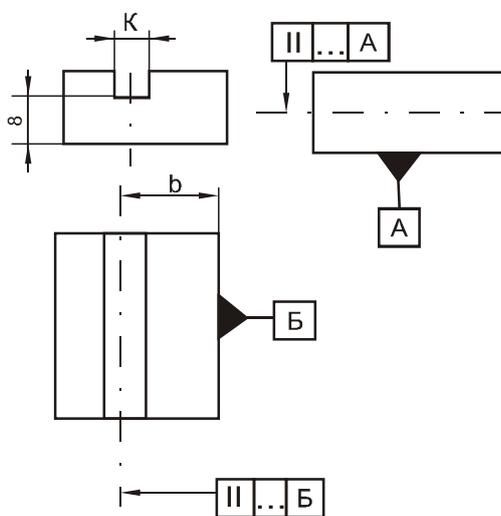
Операционные требования к точности фрезерования паза в призматической заготовке
